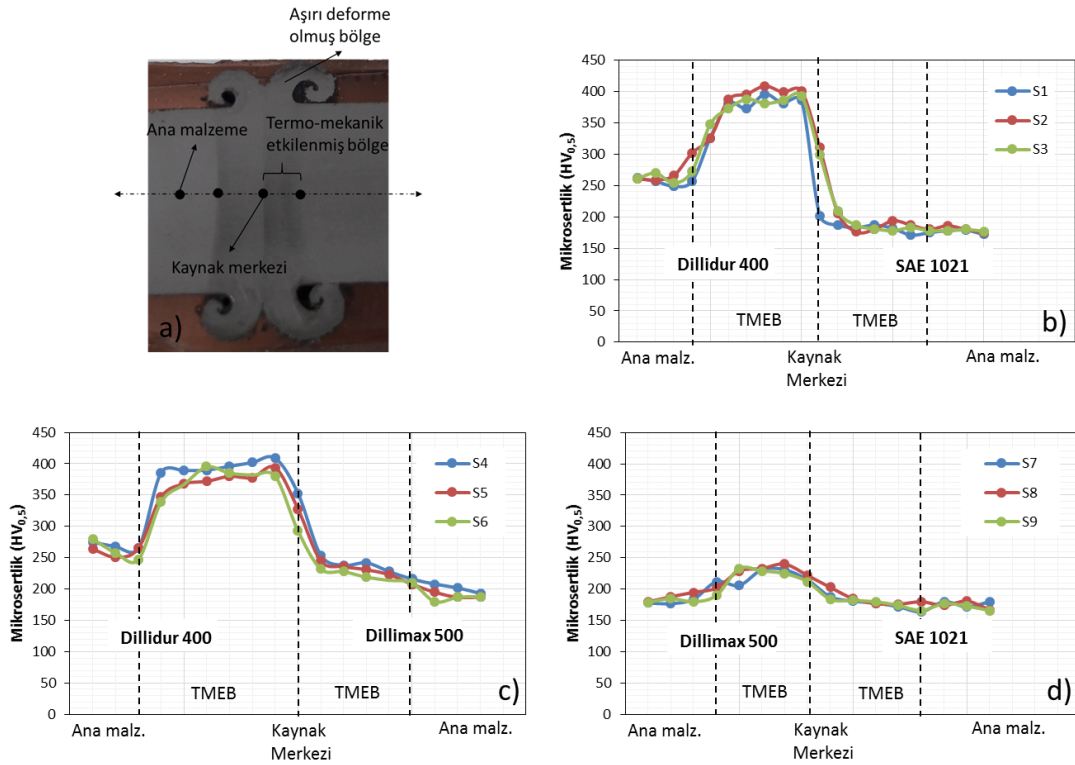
Sürtünme kaynağı ile birleştirilen numunelerin makro görüntüsü (Macro image of samples joined with friction welding)
